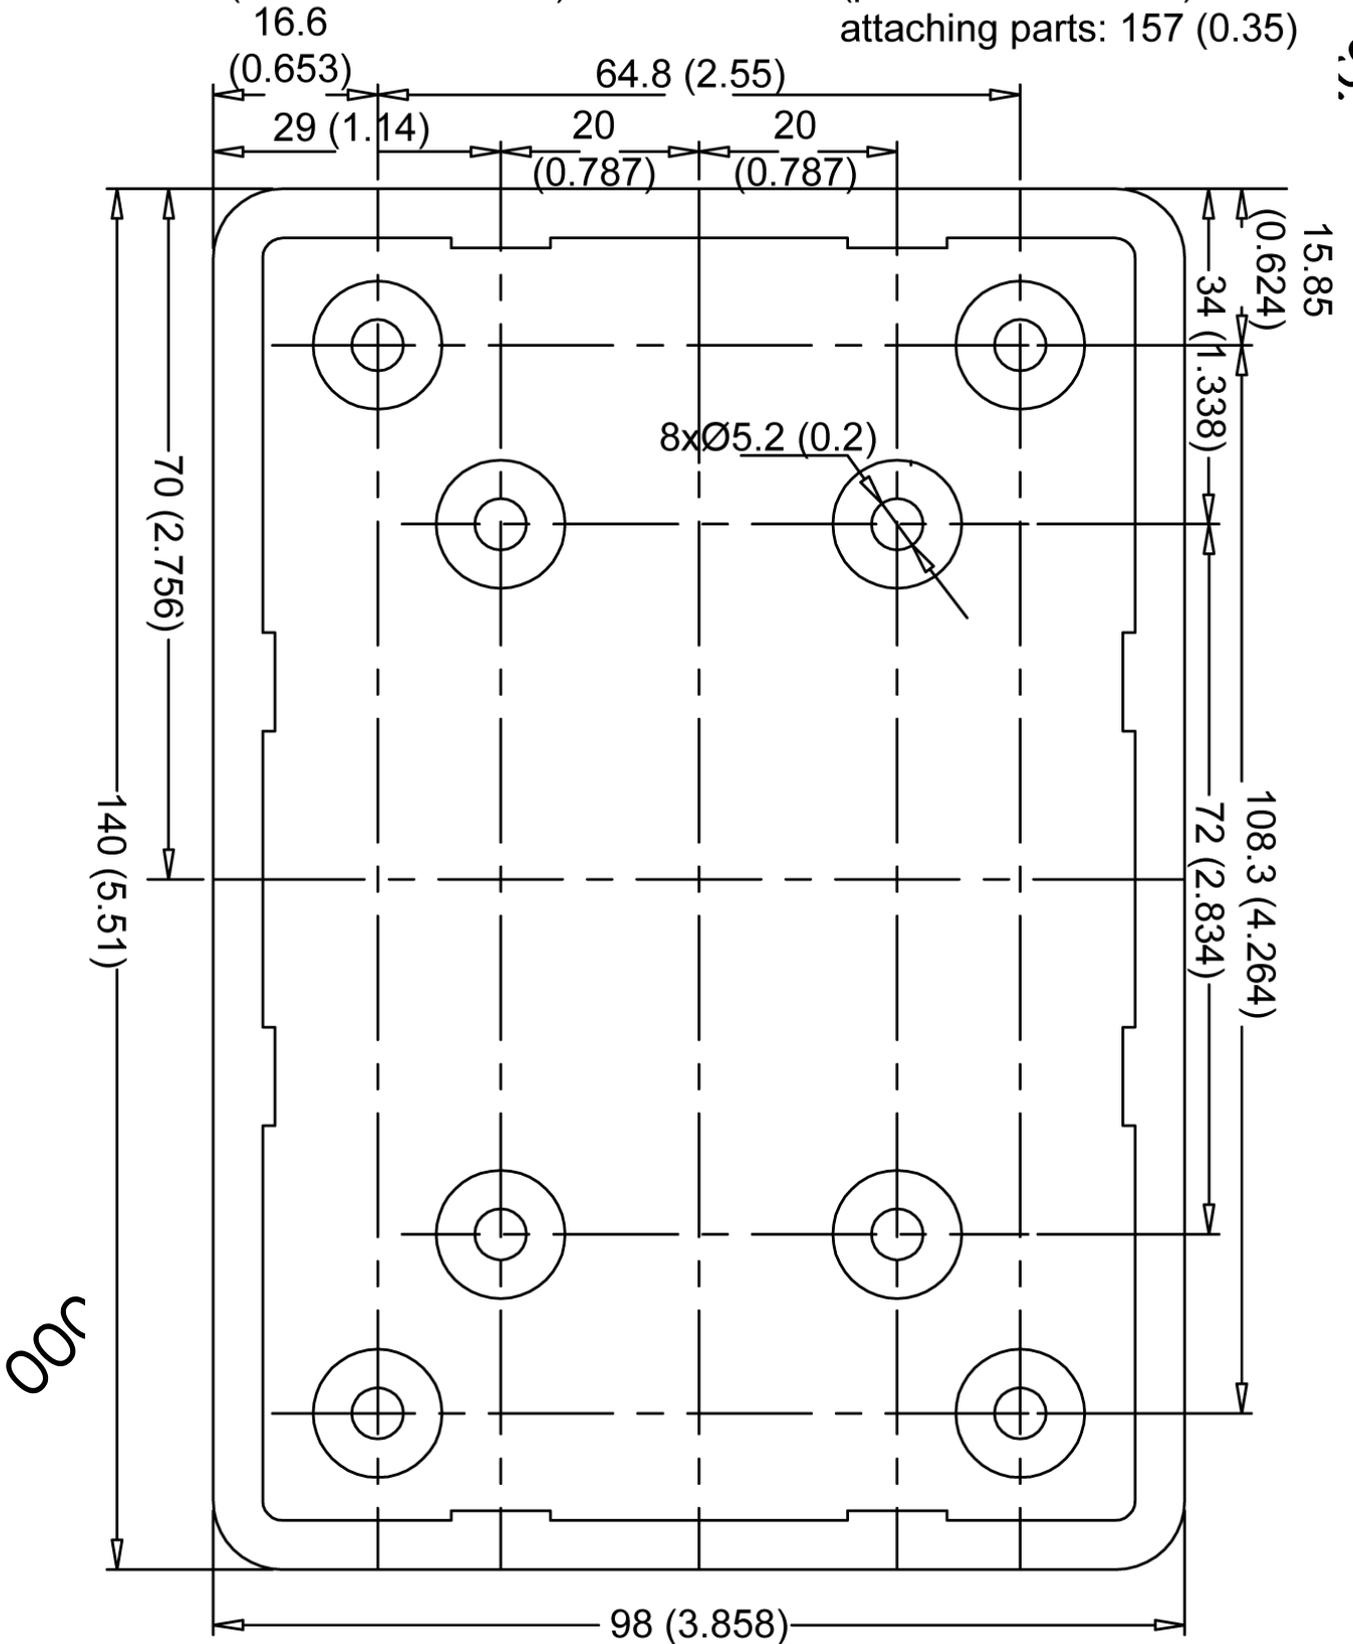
Компактный универсальный монтажный кронштейн (S1840502-02), шаблон для сверления
